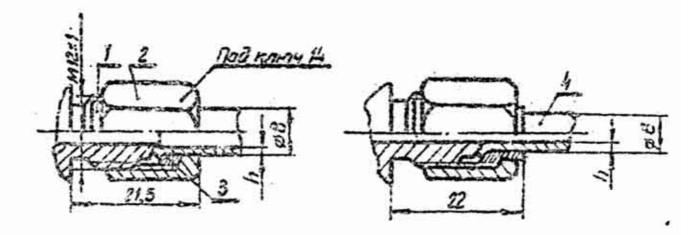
Габаритымо, установочные и присоединительные размеры ПП2.5-М1
